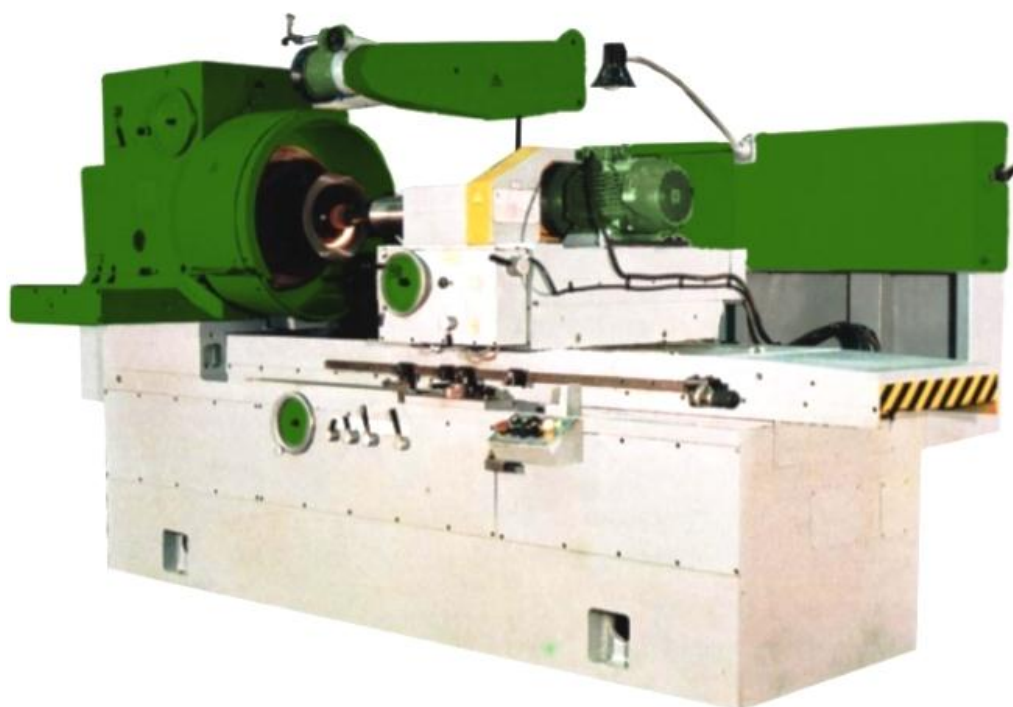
внутришлифовальный станок универсальный 3К229А
